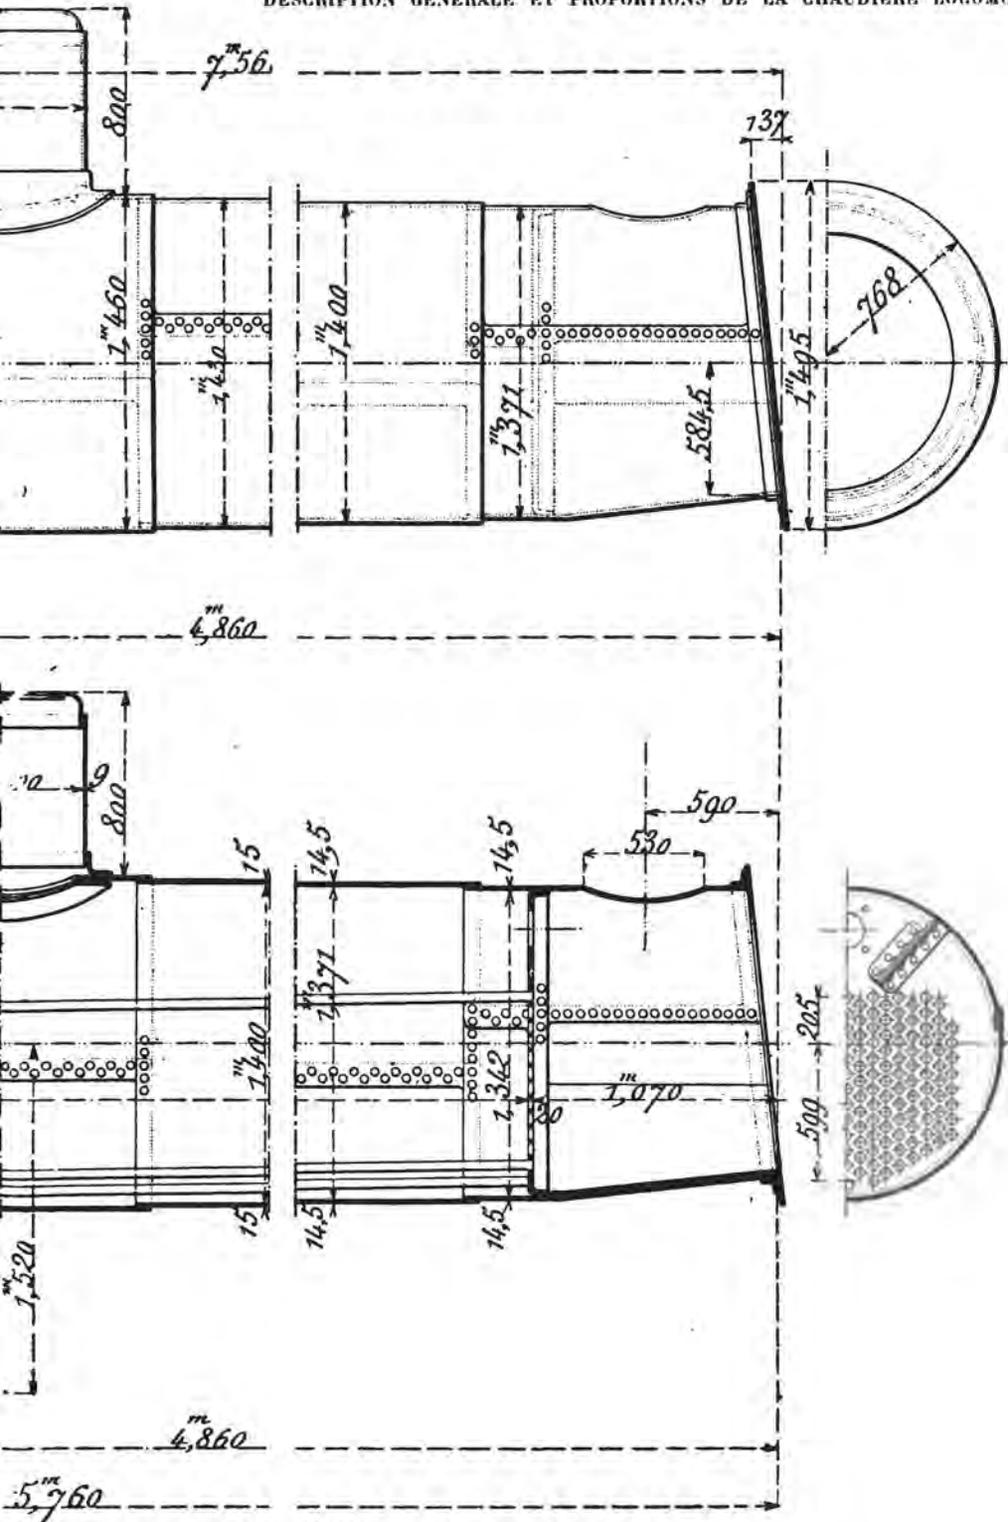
Type de chaudière locomotive. Machines à marchand
